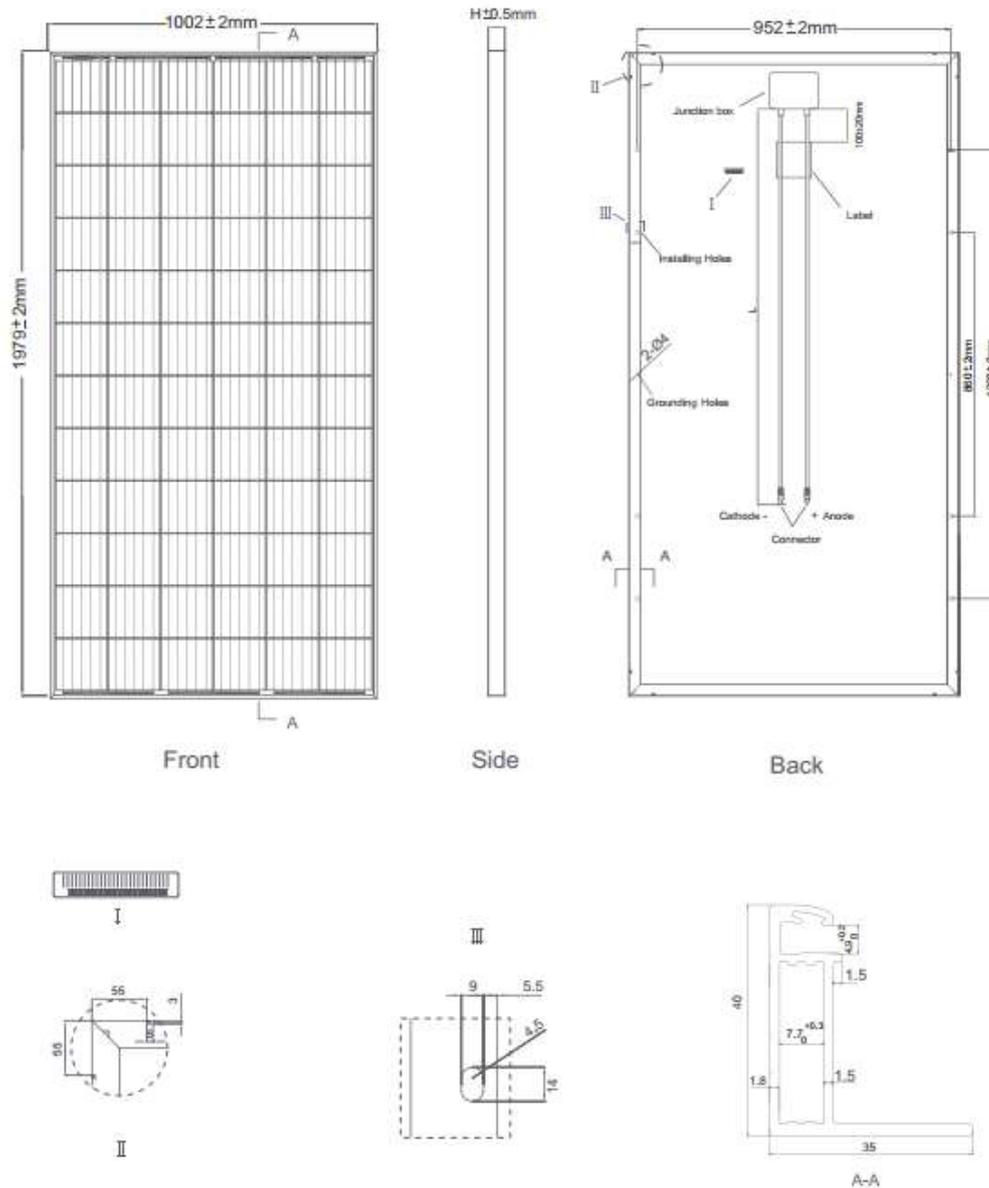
Dimensiones mecánicas del panel fotovoltaico JKM390M-72
